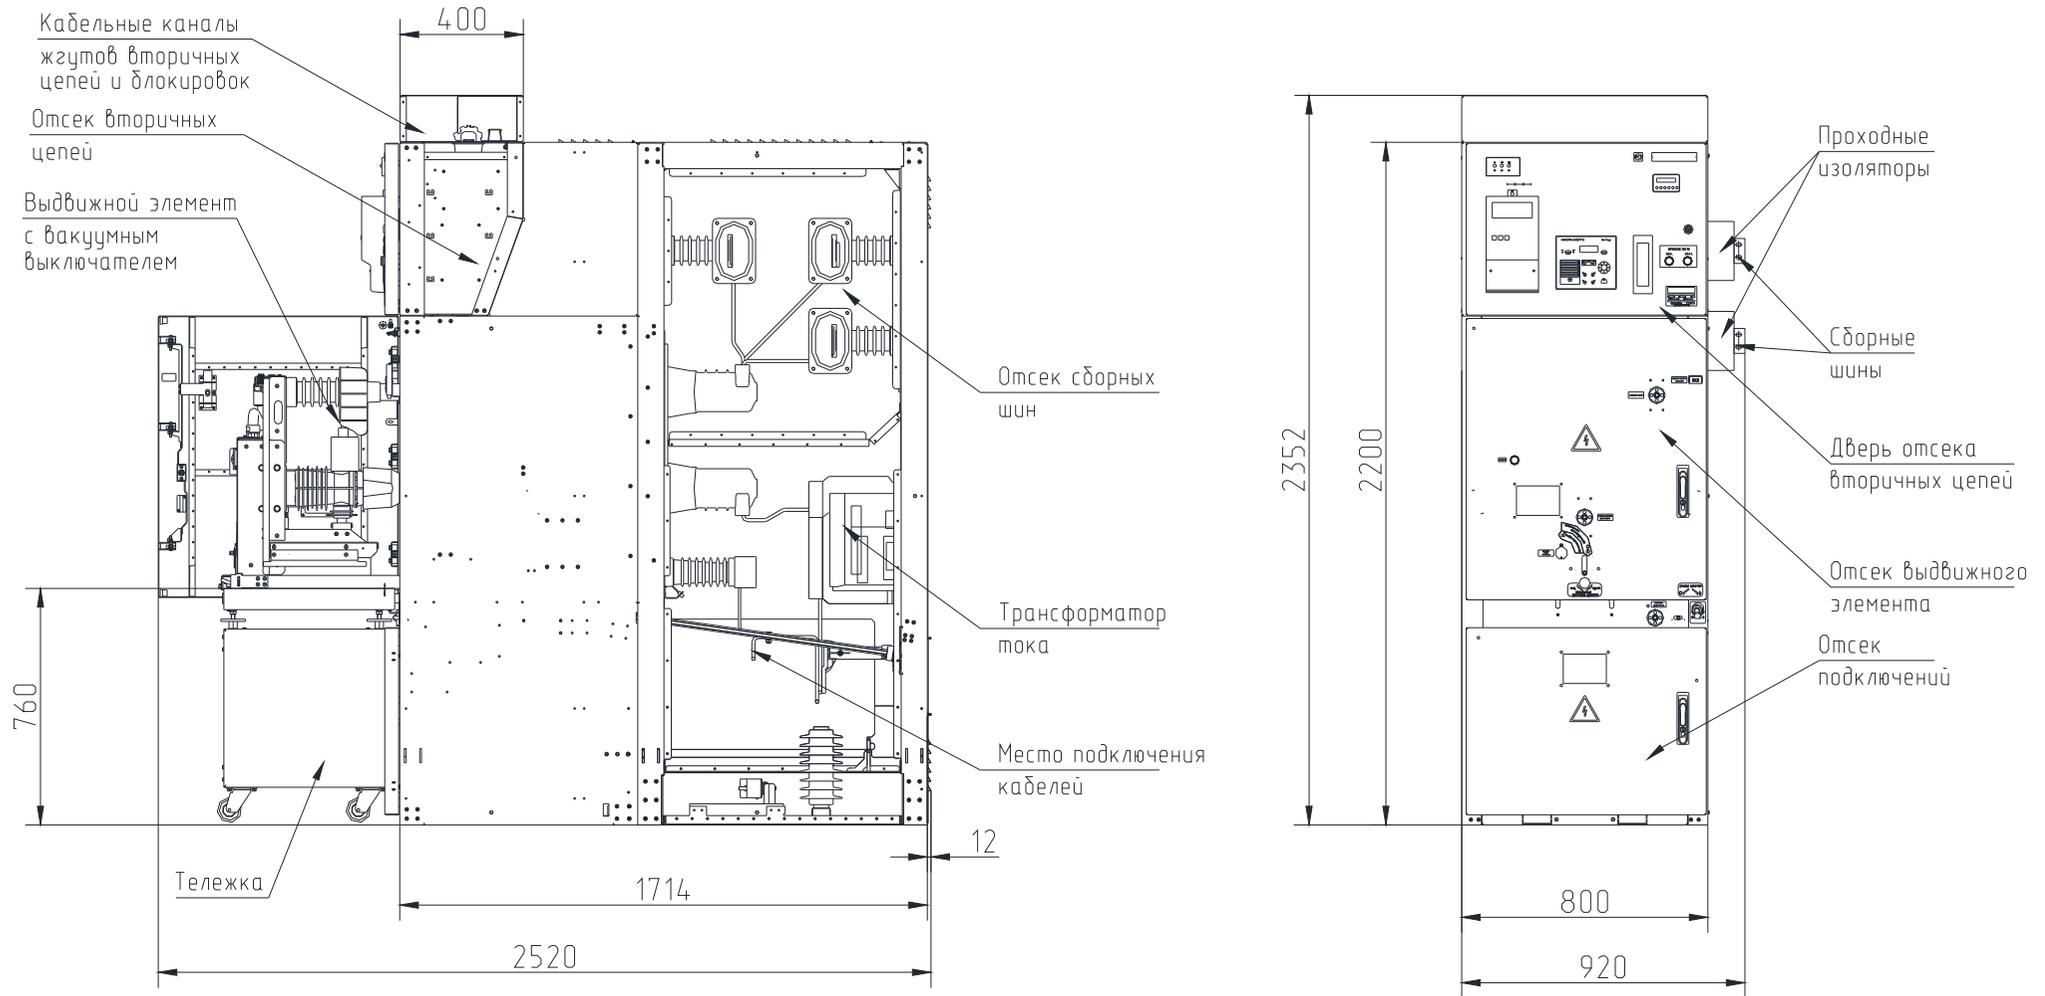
Габаритные размеры и компоновка шкафа КРУ "БЭМ-1".
